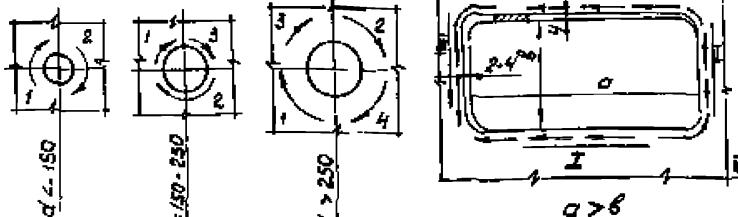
Многослойная сварка стыков обратноступенчатым методом
